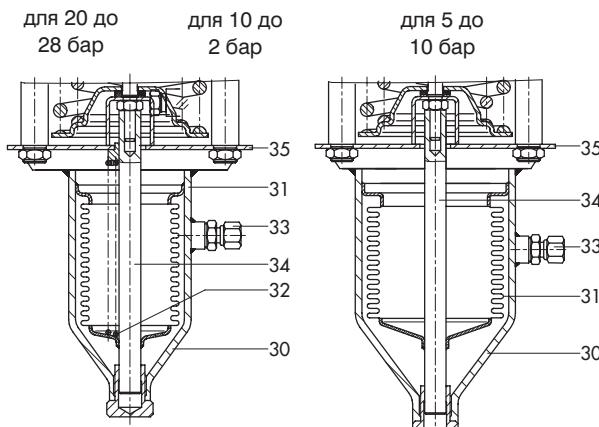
· Универсальный редуктор давления тип 41-23, принцип действия
